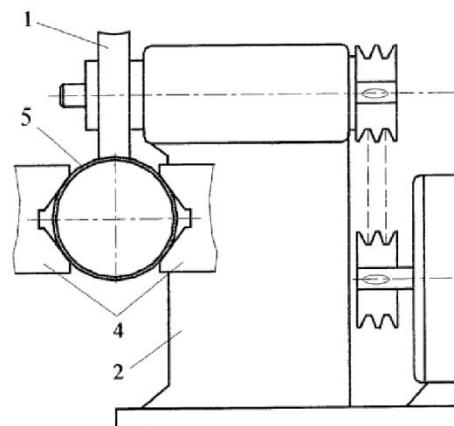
Схема установки для сварки кромок по патенту РФ2265493: 1 – диск; 2 – станина; 3 – электродвигатель; 4 – призмы сжимающие; 5 – свариваемая обечайка.
